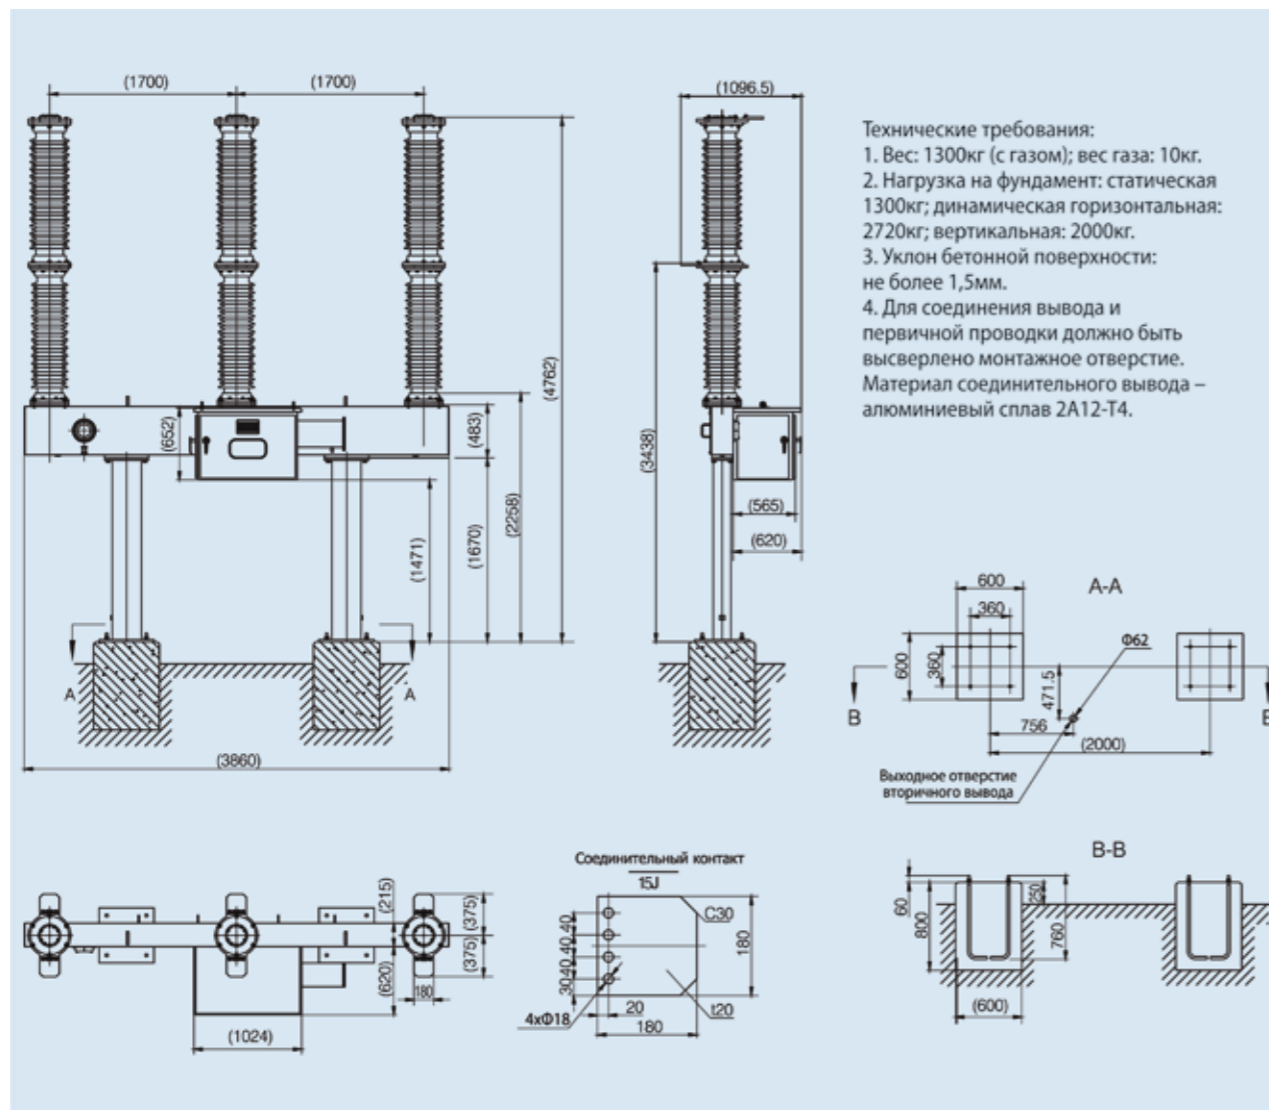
Внешний вид и размеры выключателя высоковольтного элегазового выключателя LW36-126
